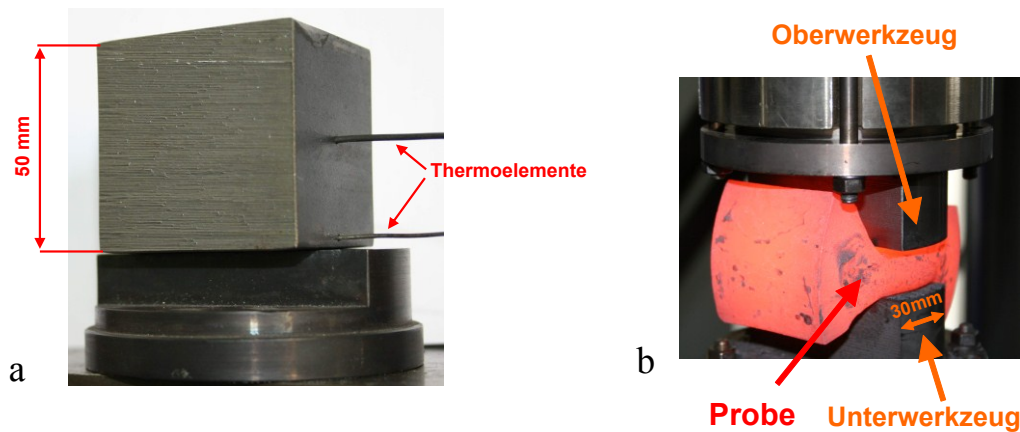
a) Unterwerkzeug mit instrumentierter Probe, b) Umformprozess
